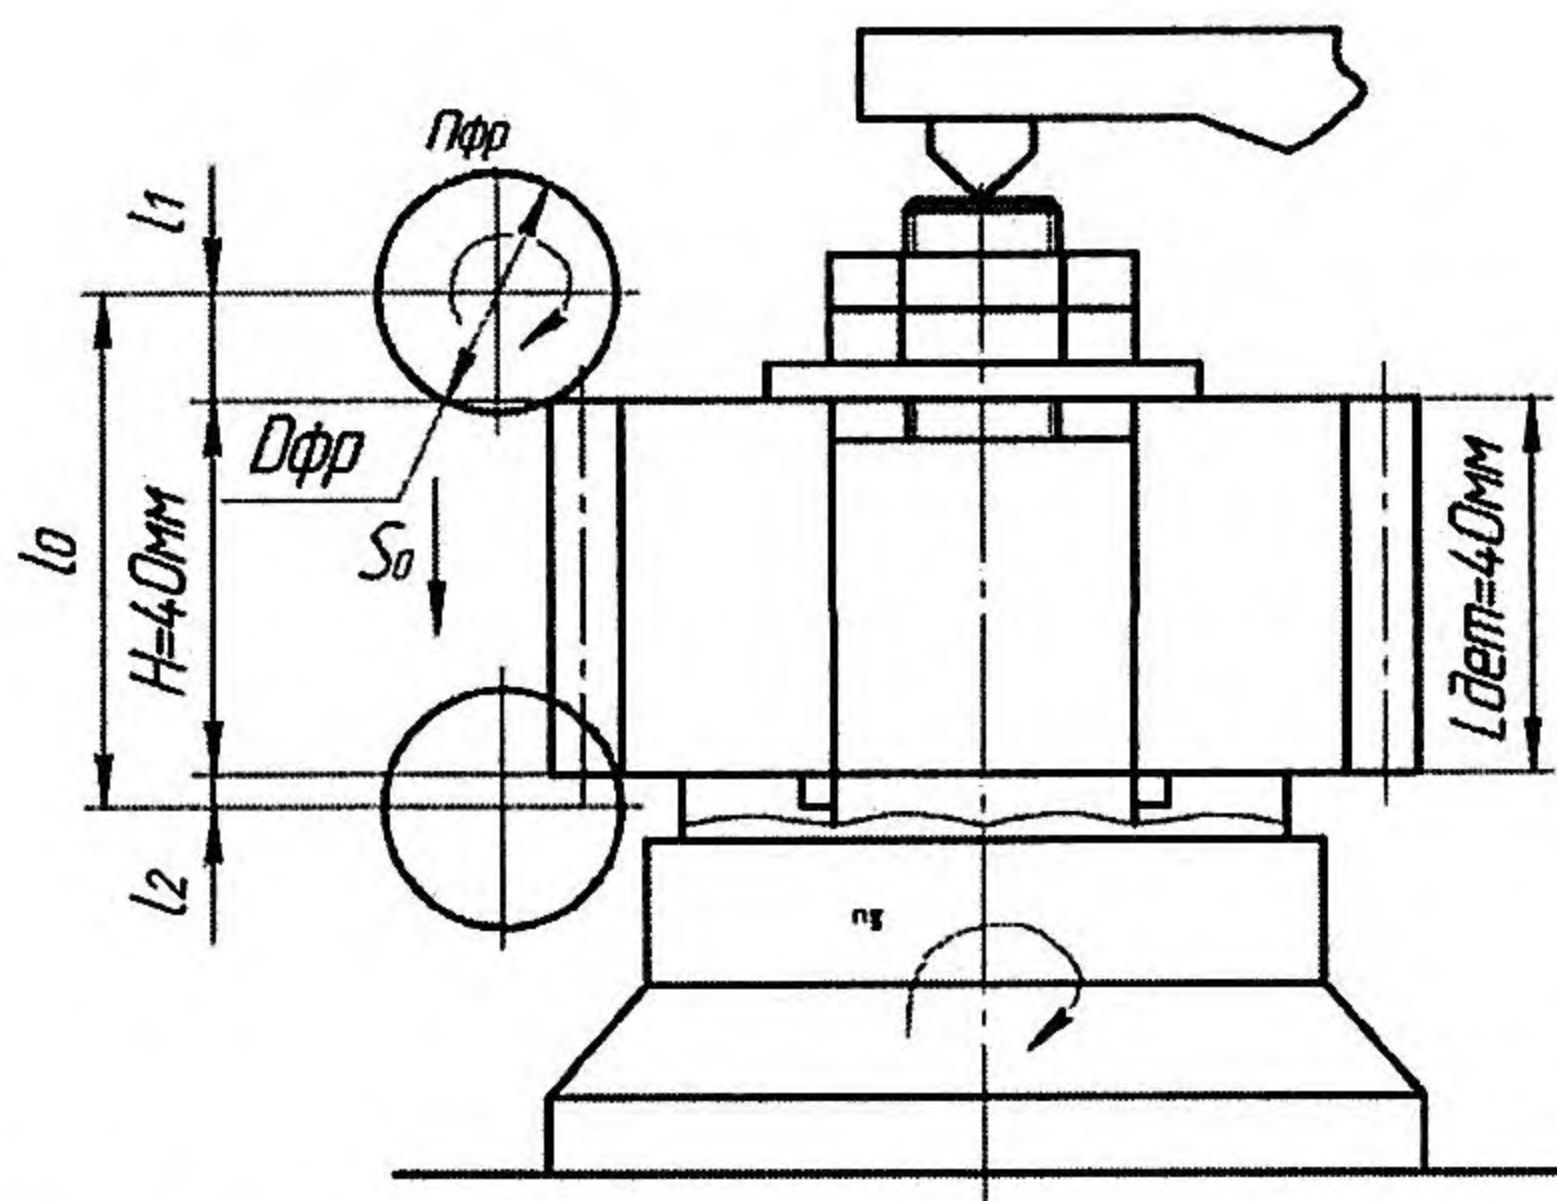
Схема обработки колеса на зубофрезерном станке
